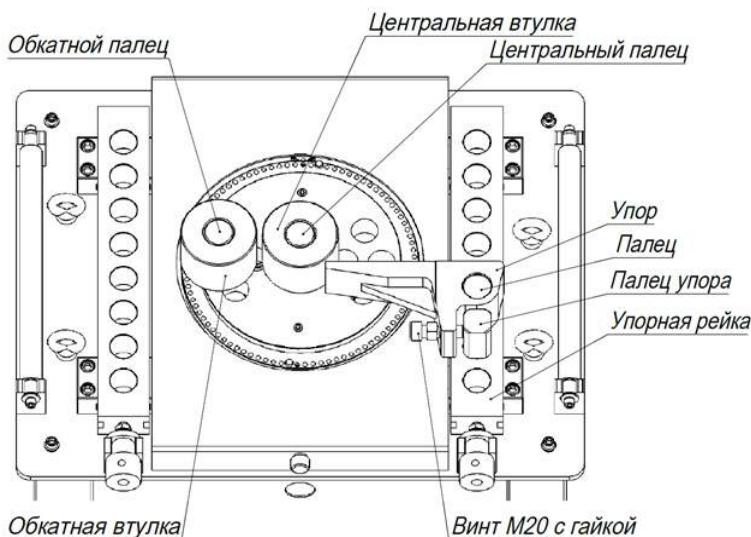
Схема расположения гибочных приспособлений (VPK Г-55)
